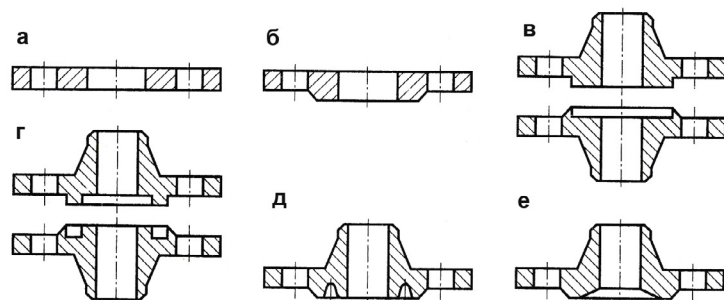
Форма поверхности фланца (вид «зеркала»):
